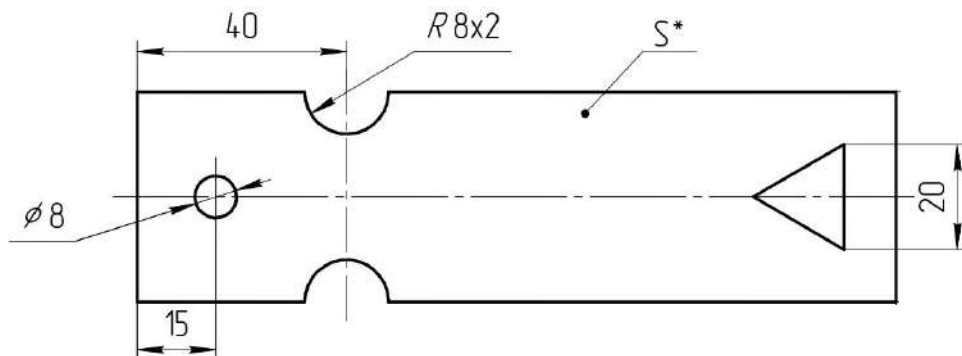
Пластина с частично указанными размерами (вариант образца изделия)
